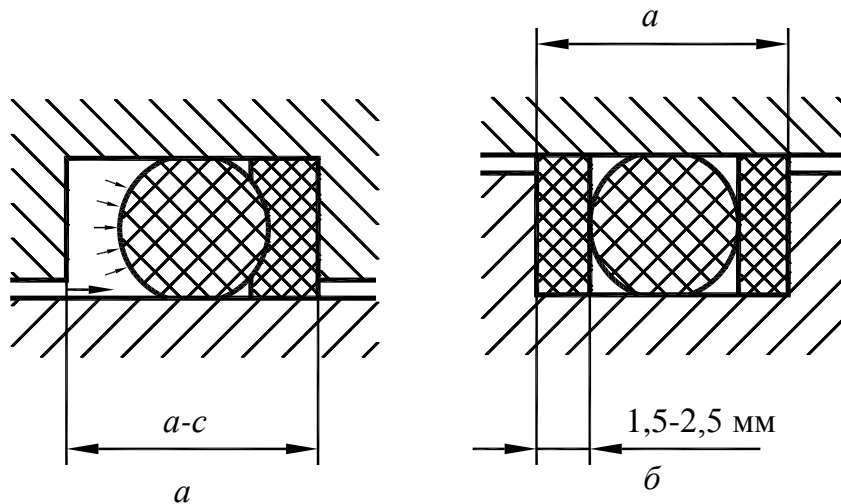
Уплотнение резиновыми кольцами с защитными проставками
